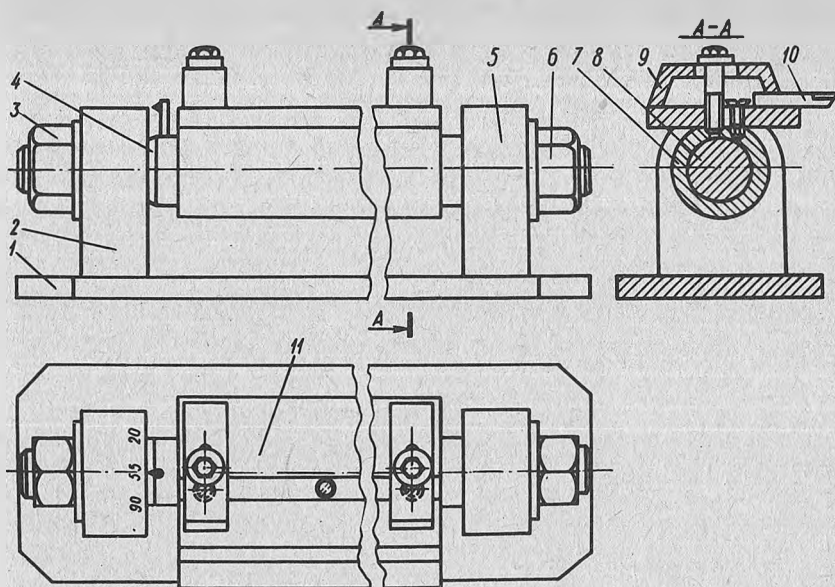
Приспособление для заточки и доводки ножей с пластинками твердого сплава на универсально-заточных или плоскошлифовальных станках.
